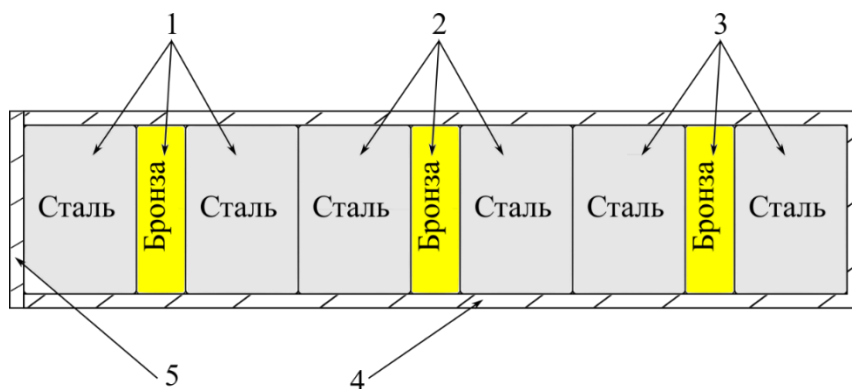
Схема укладки образцов из стали 12Х18Н10Т и бронзы Cu-Cr в контейнер для диффузионной сварки: 1 - 3 - сборки сталь - бронза - сталь, обработанные по режимам 1, 2 и без лазерной термообработки, соответственно; 4 - тонкостенный контейнер, 5 - крышка контейнера.
